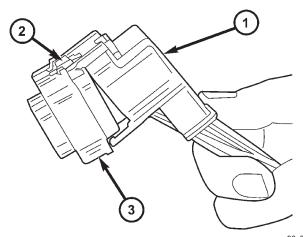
DESMONTAJE DE CUBIERTA DE GUARNICION
